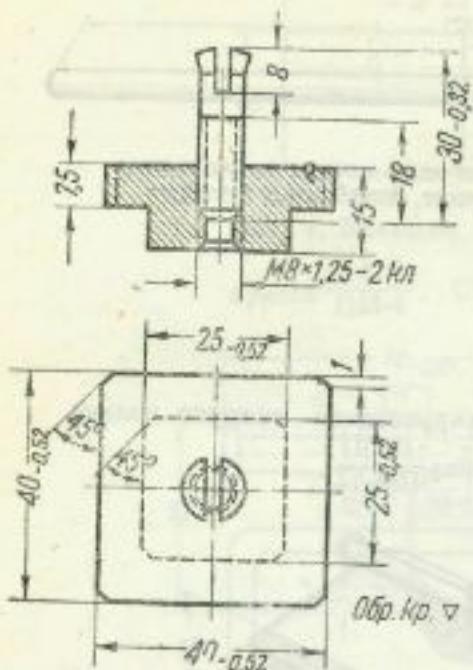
Приспособление для прорезки шлица на срезе втулки к ушкам дна короба ПМ-17
